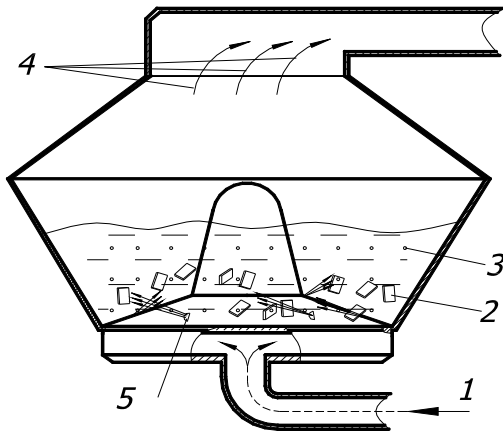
Схема действия струй сжатого воздуха на детали и абразивный материал в жидкости: 1 – сжатый воздух, 2 – обрабатываемая деталь, 3 – абразивное зерно, 4 – отработанный сжатый воздух, 5 – воздушное сопло.
